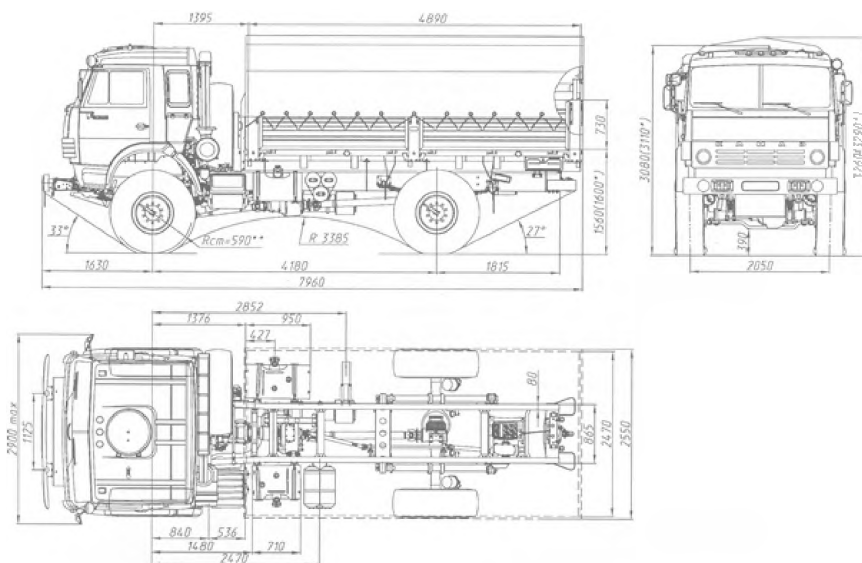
Автомобиль-тягач КАМАЗ-4350. Габаритные размеры.
